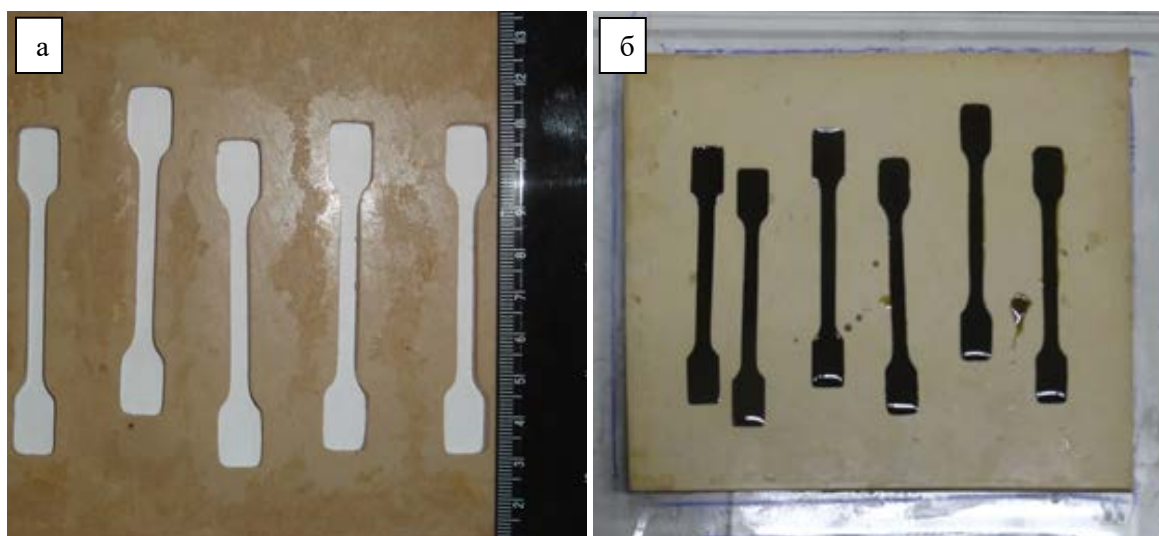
Внешний вид формы для изготовления образцов: а) пустая; б) заполненная ЭС
